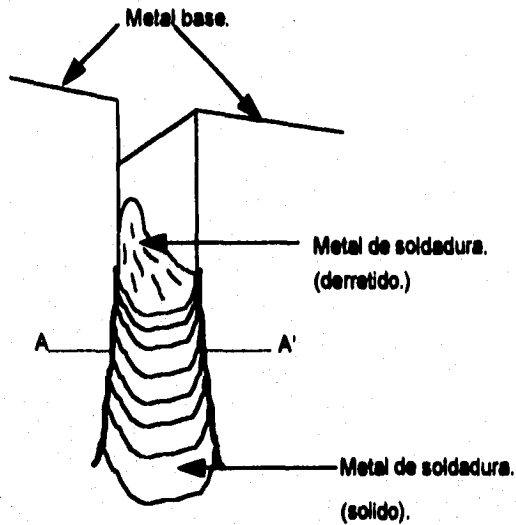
, dibujo esquemático de una soldadura, mostrando el movimiento en el charco soldado.
